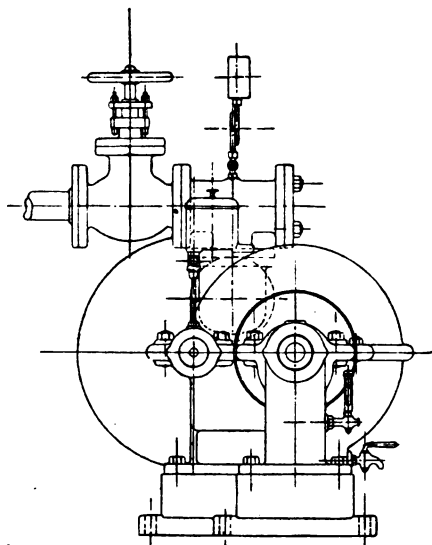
Seitenansicht einer 30 pferdigen de Laval-Turbine.
